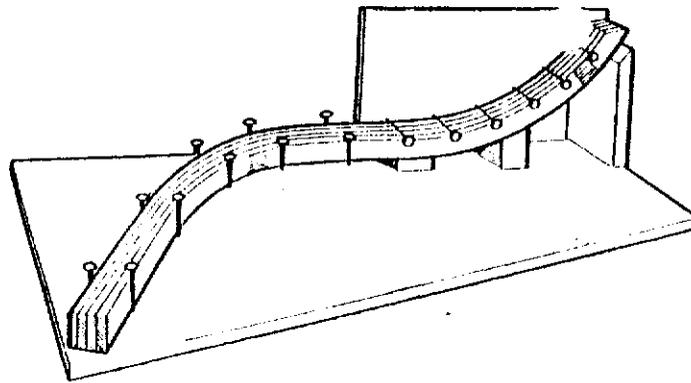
Cintre contre-coudé sur un montage de collage avant la mise en place des serre-joints.
